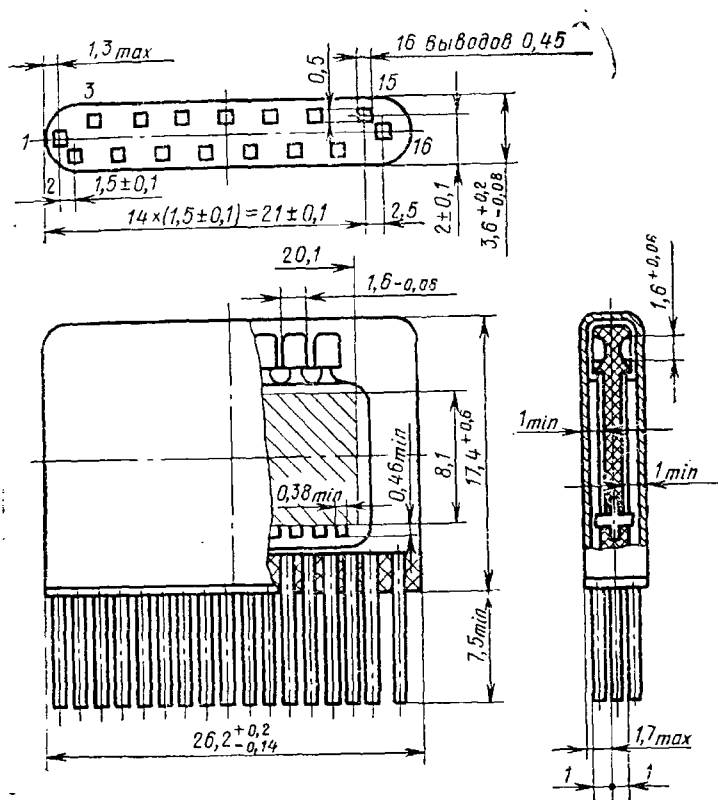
Конструкция металлополимерного корпуса «Пенал»
